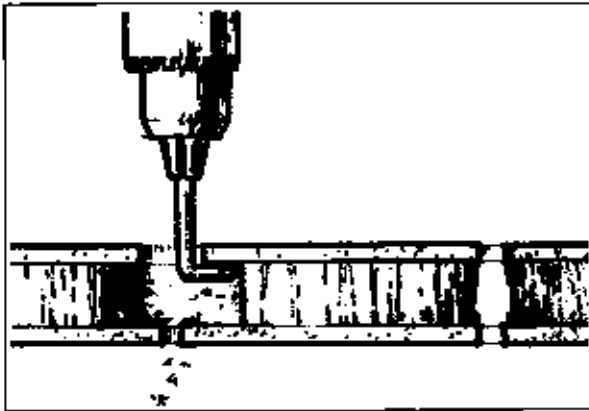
Entfernen Sie den Kern um das Loch herum etwa 12 mm weit mit einem gebogenen Nagel oder einem Innensechskant-Schlüssel.
